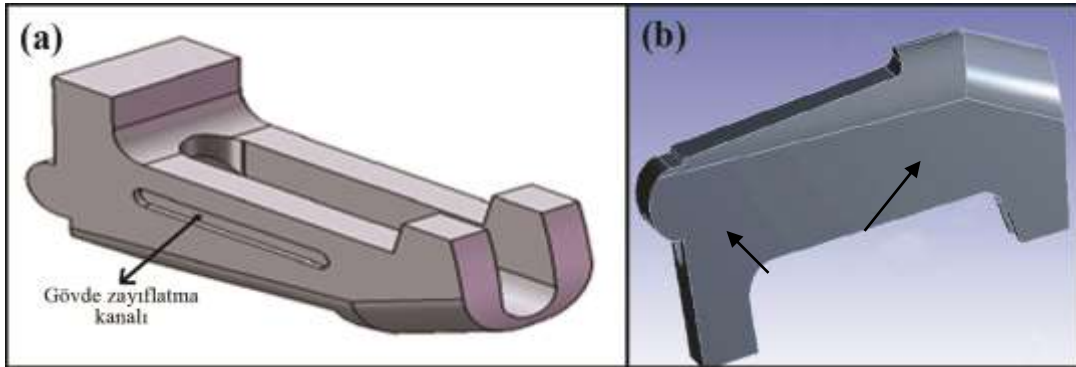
Hali hazırda kullanılan Kilit parçasının geometrik özellikleri (mm)
